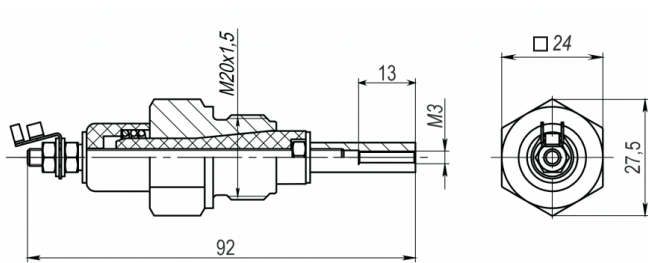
габаритные и установочные размеры датчика КДУ-1Э
